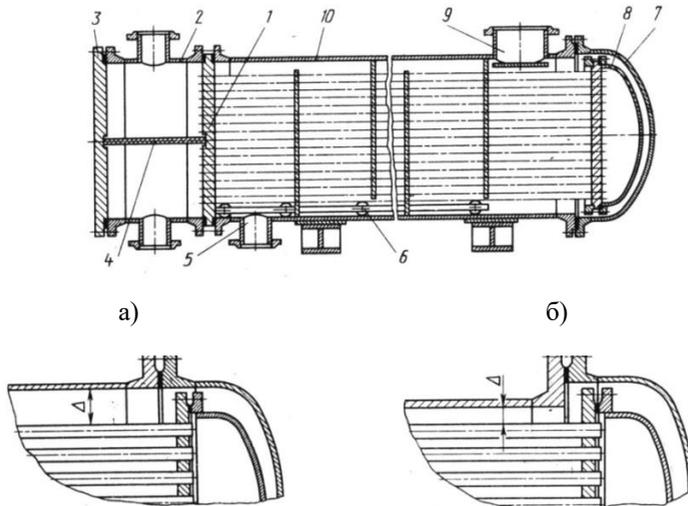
Горизонтальный двухходовой КТТ с плавающей головкой
